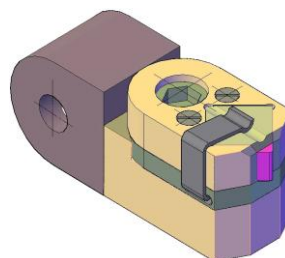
Резцовая головка с механическим креплением режущей пластины
